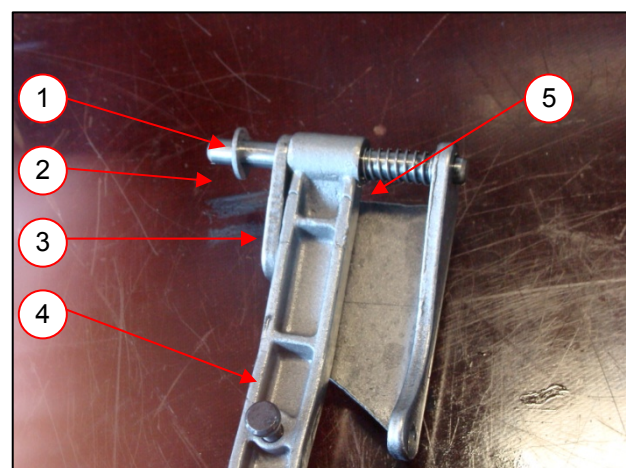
Порядок установки деталей на ось двуплечего рычага
